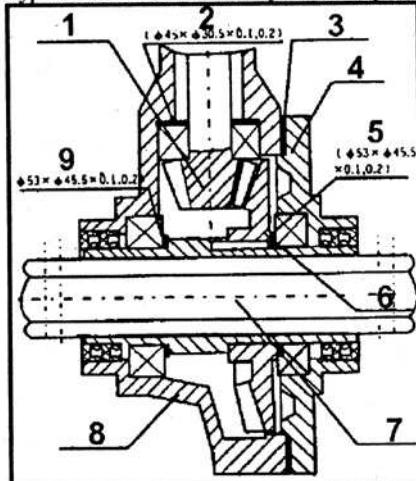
Структурная схема конической зубчатой передачи в корпусе трансмиссии
